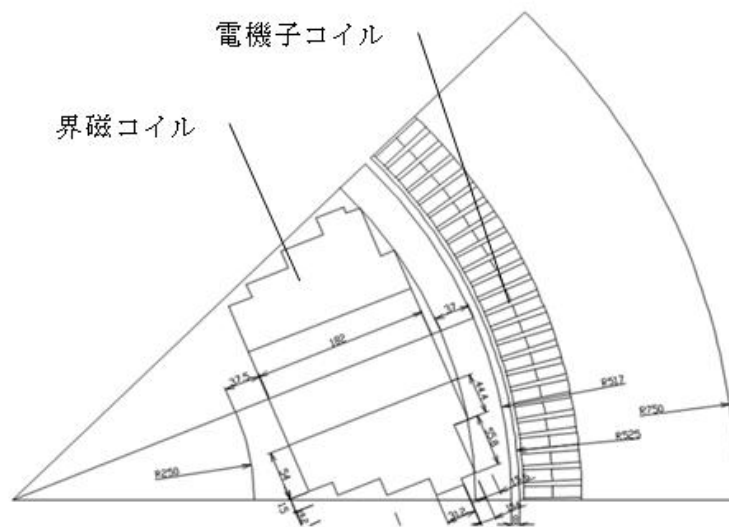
5MW 回転機 菱形傘型モデルコイル断面図
